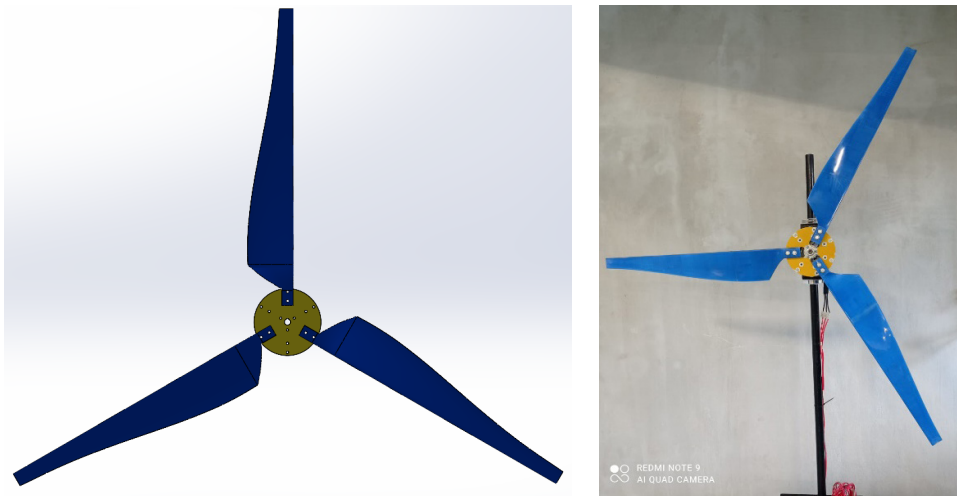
Diseño del rotor (izquierda) y rotor manufacturado (derecha). Fuente: los autores.
